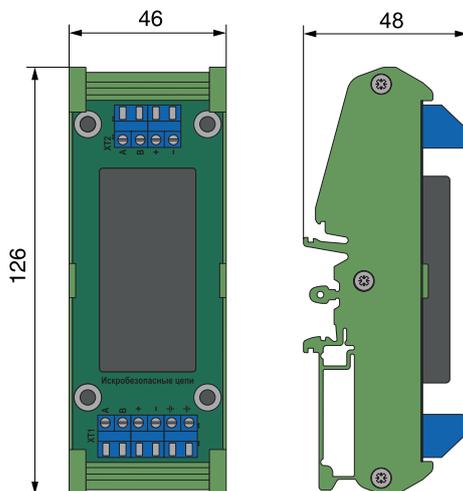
Габаритные размеры барьеров ЭНИ-БИС-113, 115, 118-Ex-DIN
